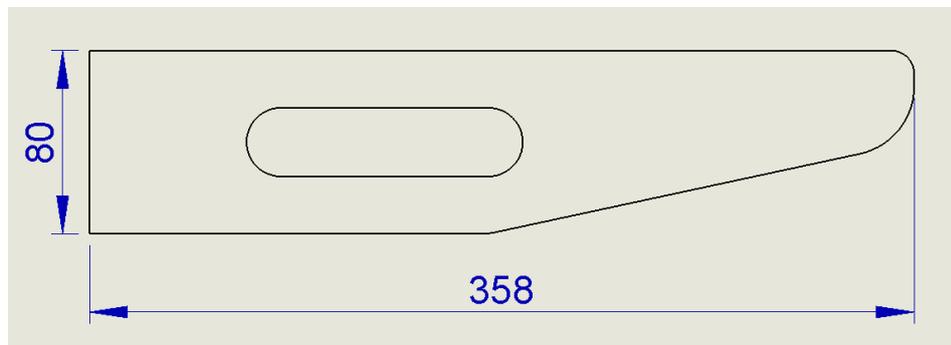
Croquis de diseño de palas removedor de cenizas.
